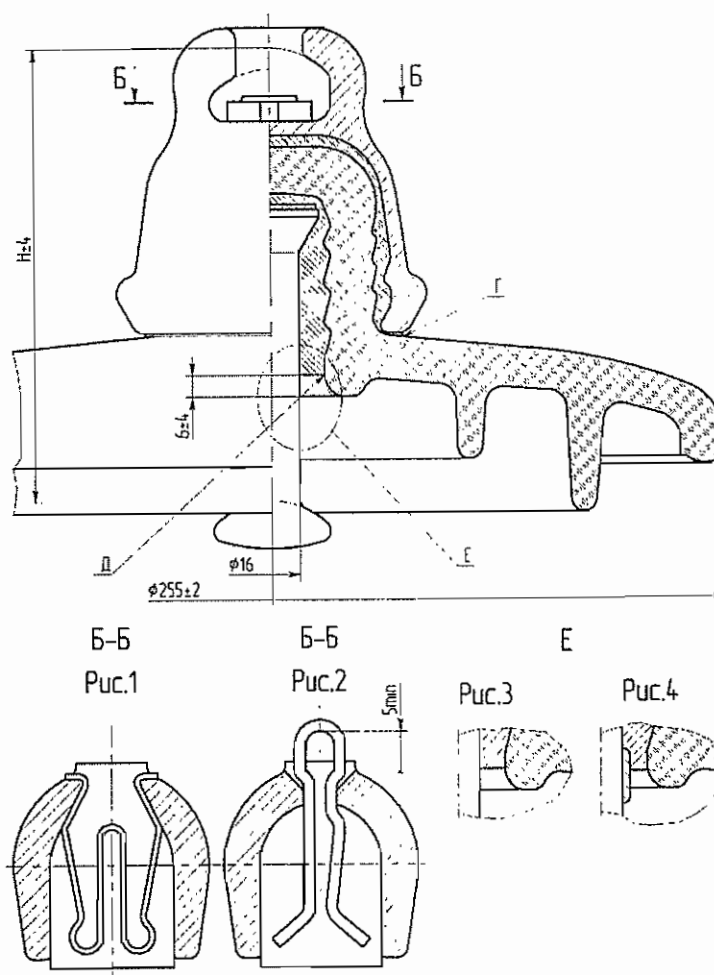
Габаритные, присоединительные и установочные размеры изолятора ПСВ 120Б
